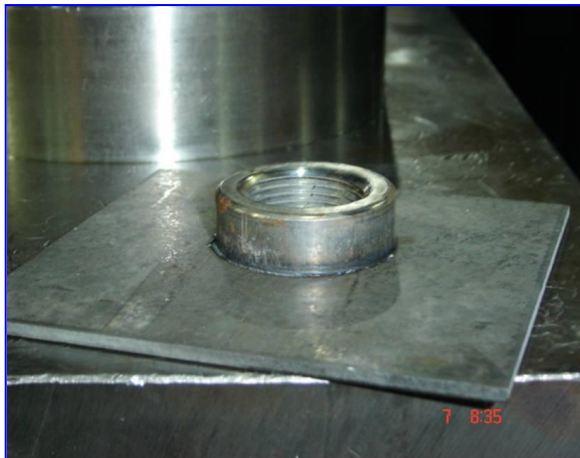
Cupón soldado para utilizarlo en prueba de desprendimiento
